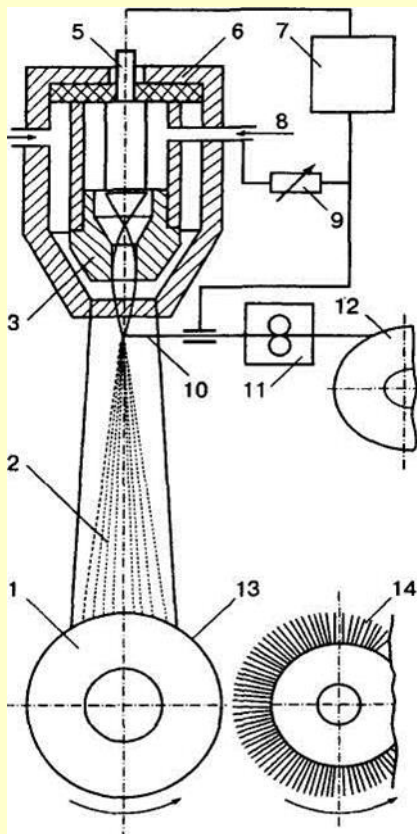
Схема плазменно-дугового напыления покрытий проволокой:
